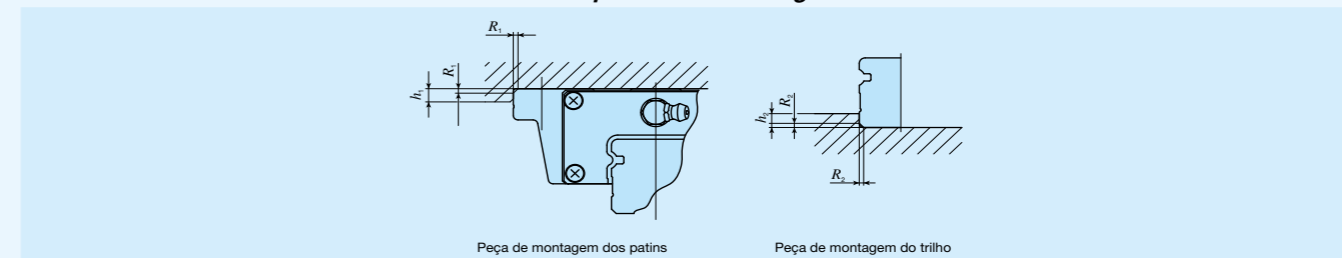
Superfície de montagem de referência e estrutura de montagem típica
